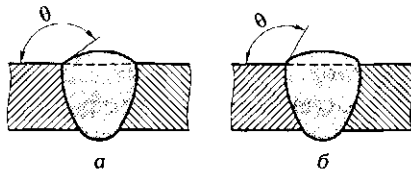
Правильный (а) и неправильный (б) профили сварного шва:
